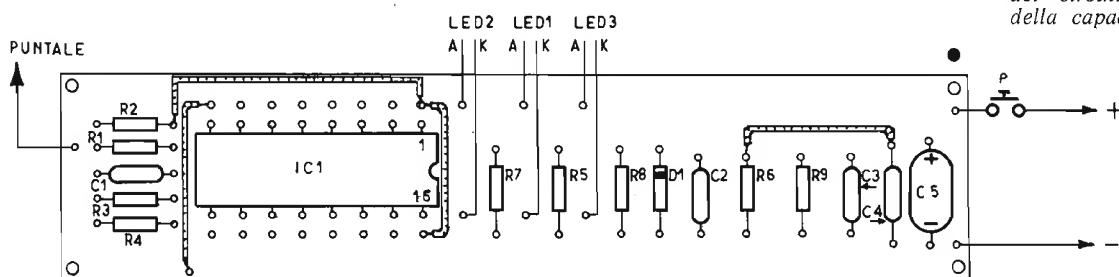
Riproduzione della stessa piastrina di supporto a circuito stampato, vista però dal lato dei componenti: il puntino nero visibile in alto a destra può essere un utile riferimento per l'identificazione del medesimo angolo rispetto al disegno di figura 2. Si noti l'orientamento del circuito integrato, del diodo D1 e della capacità C5, nonché la polarità dei
